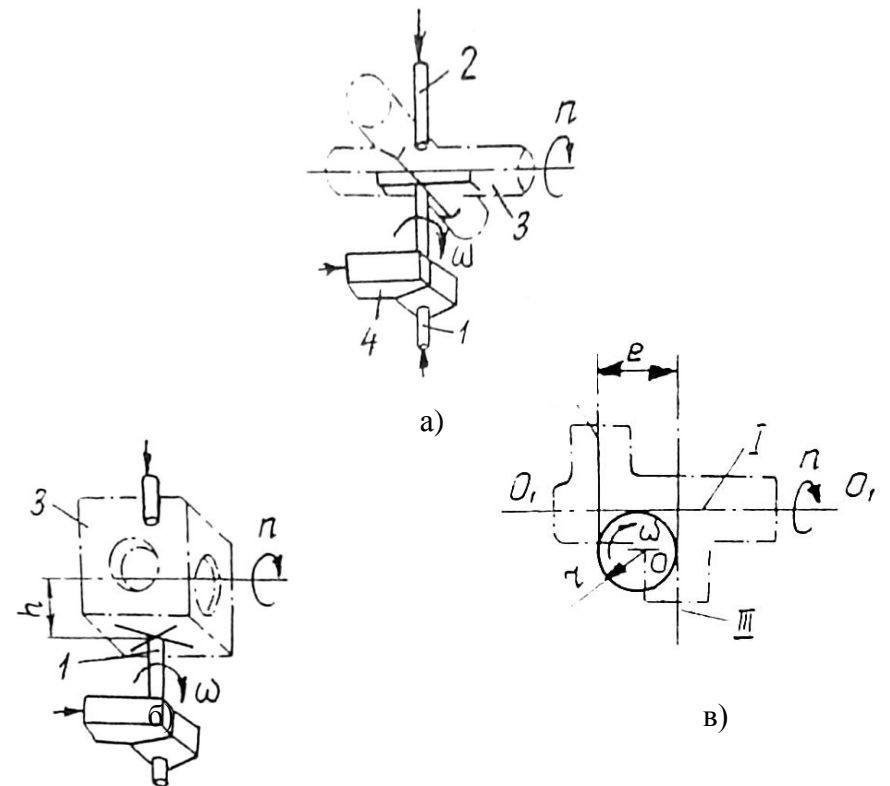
Схемы установки (базирования) и фиксации в угловом положении деталей при многосторонней обработке на токарных станках: а) установка детали с самоцентрированием; б) установка детали по плоскости без самоцентрирования; в) определение положения оси поворота детали со смещенными осями ( $n$  – вращение шпинделя,  $\omega$  – поворот детали)
